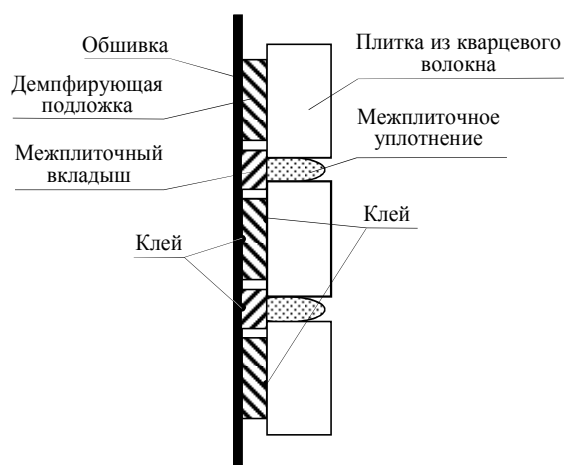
Схема крепления плиток (ТЗМК) к обшивке из алюминиевого сплава
